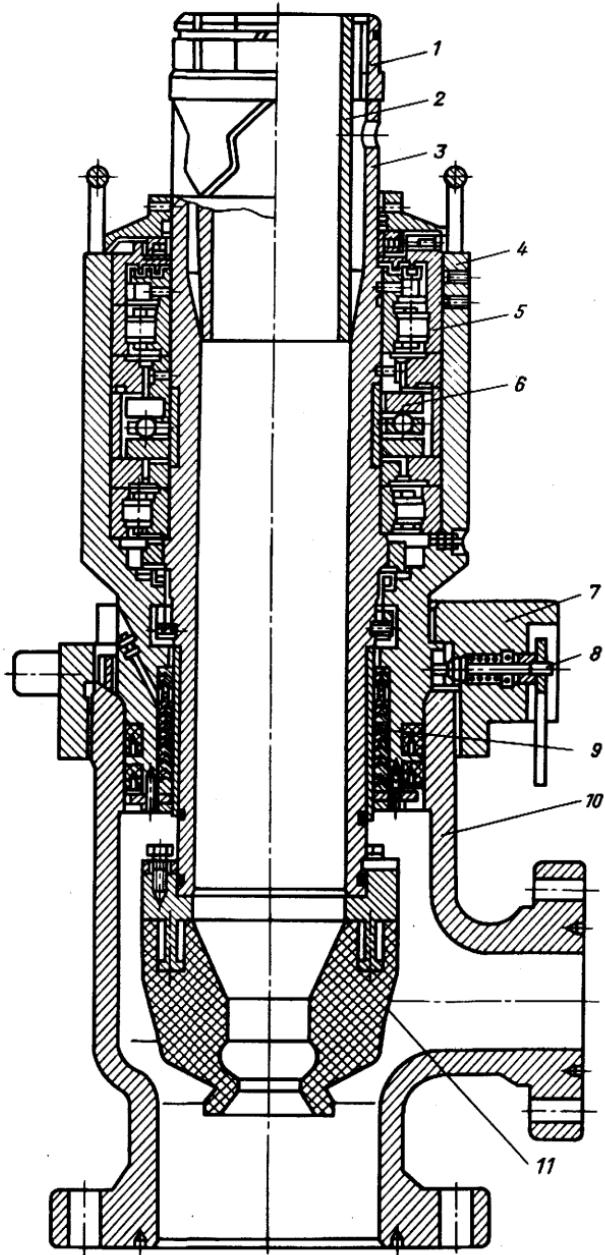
Вращающийся превентор типа ПВ с прямоточными задвижками на давление 21 МПа
